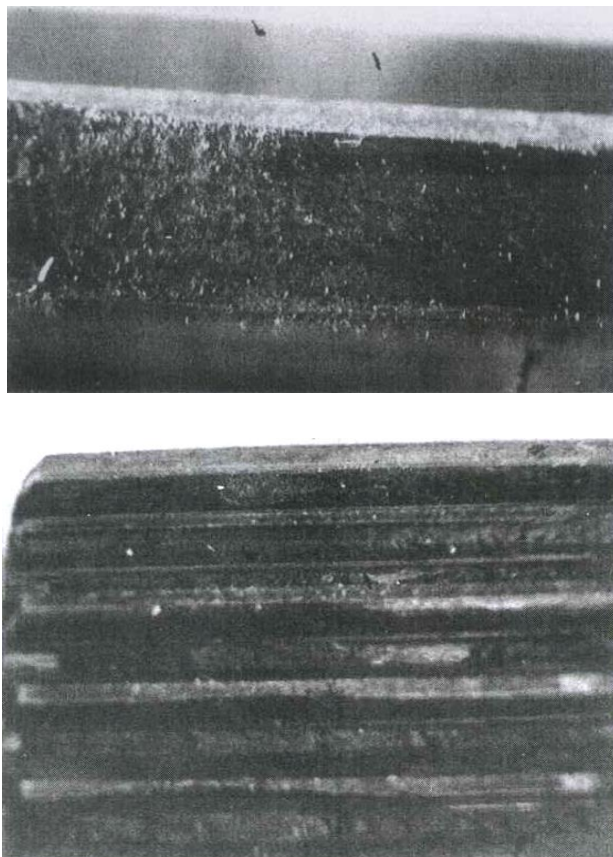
Знос контактних поверхонь шліцьових зубців вал-ресор приводу насосного агрегата
